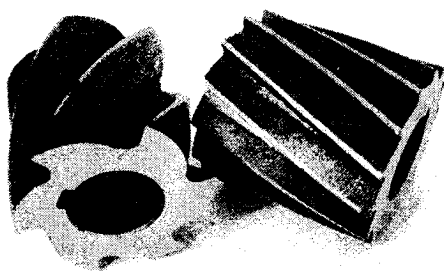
Циліндричні фрези з великими та дрібними зубами
